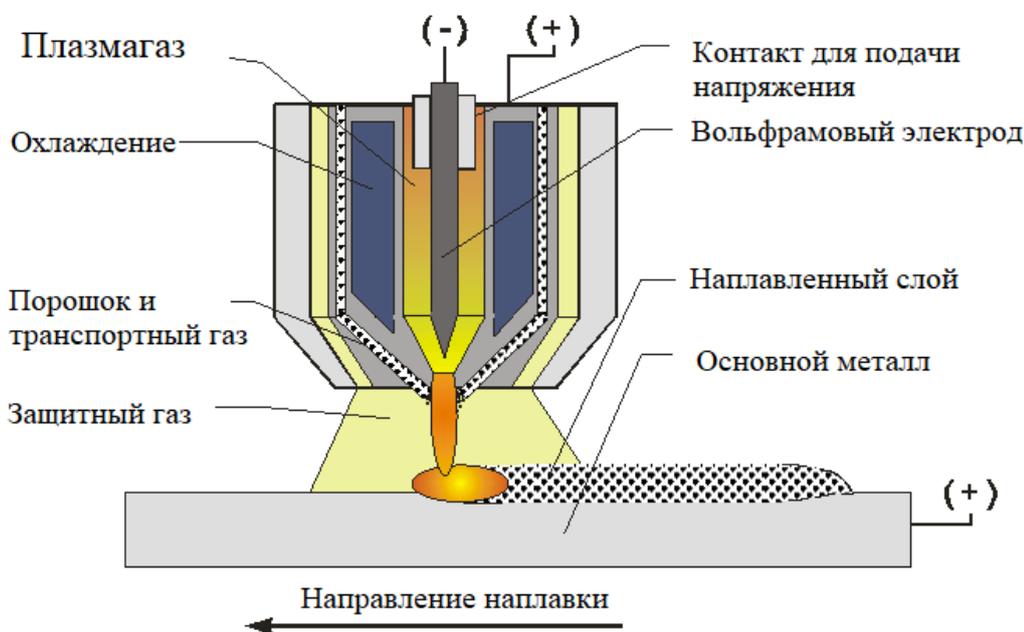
Схема плазменной наплавки с вдуванием порошка в дугу
